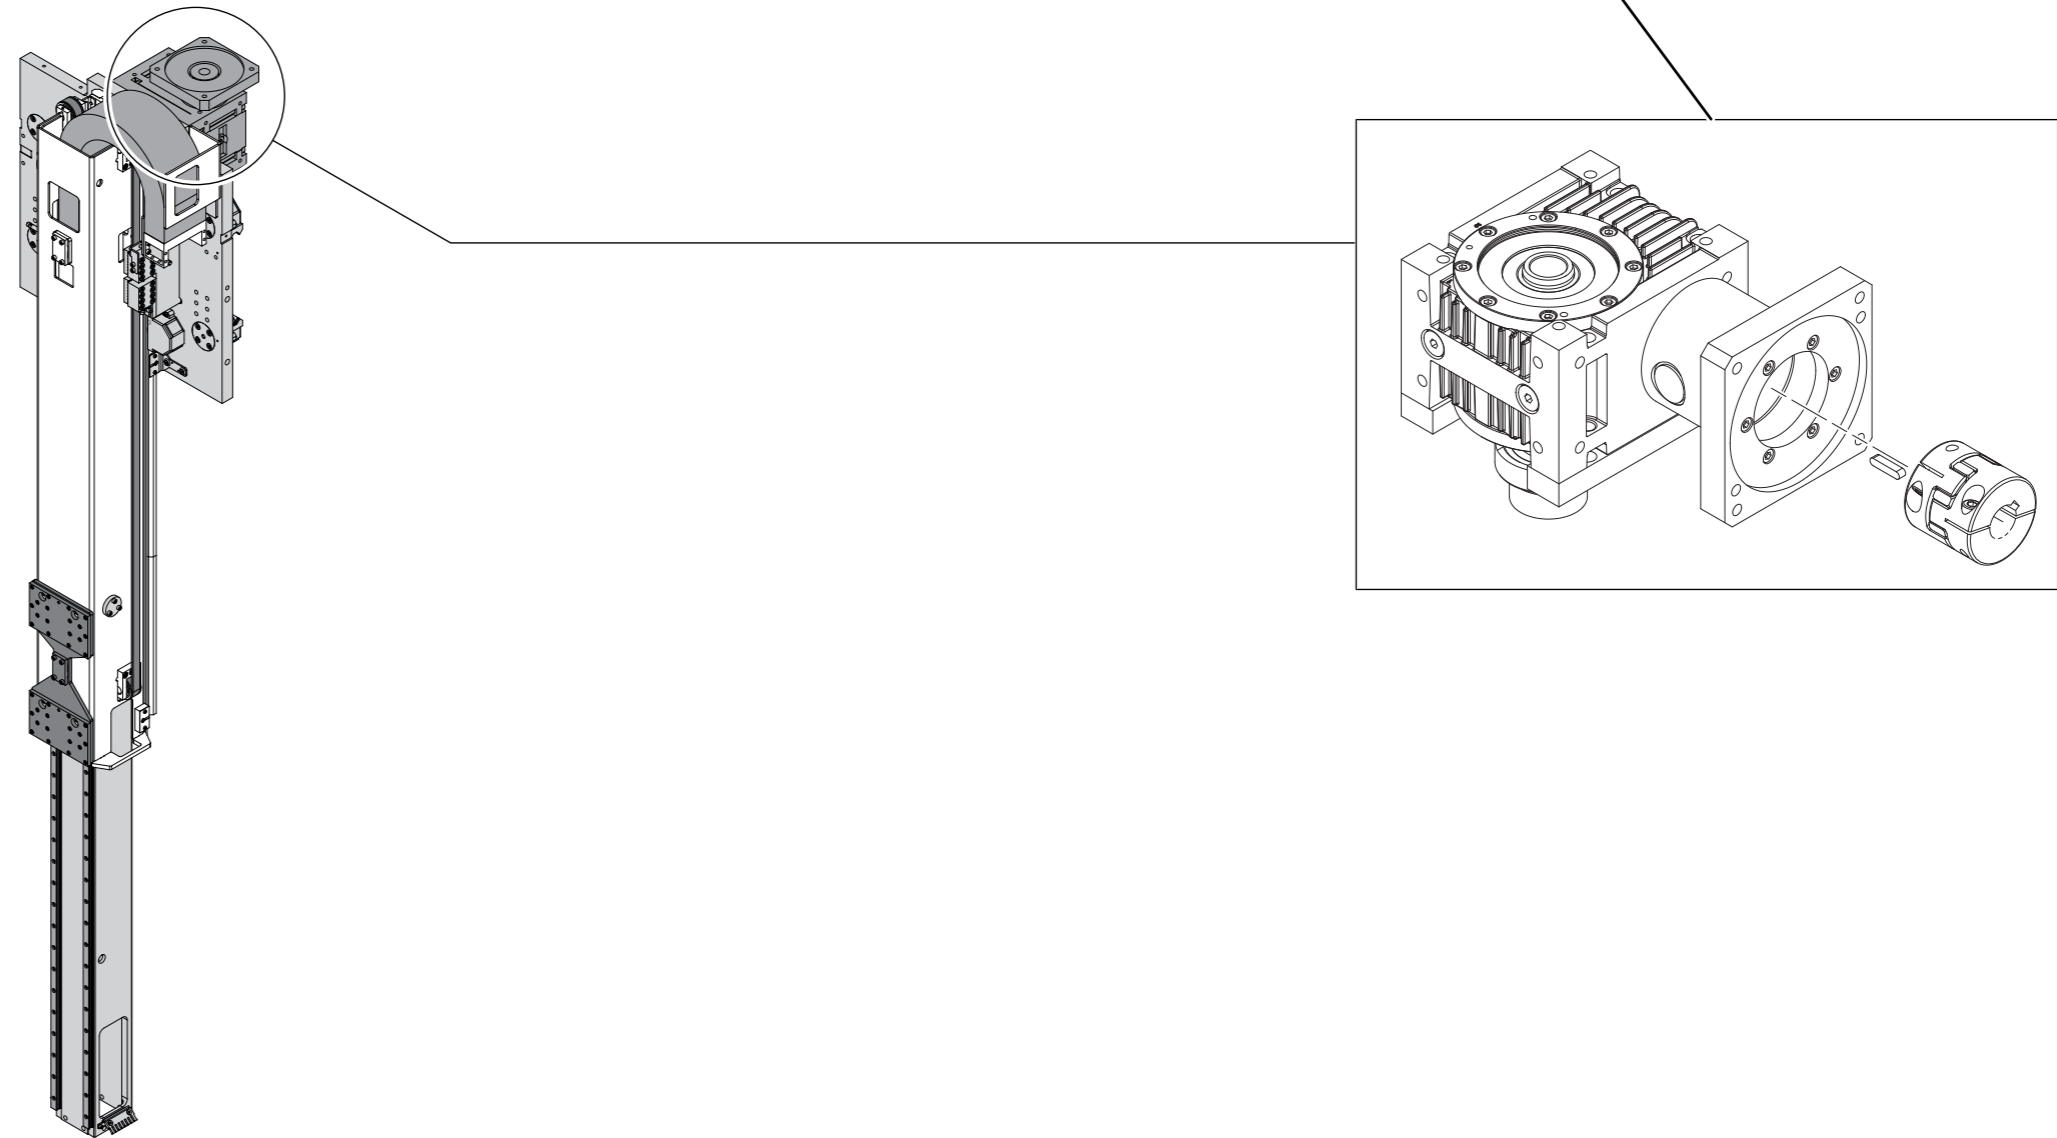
План техобслуживания: Блок редуктора Güdel
